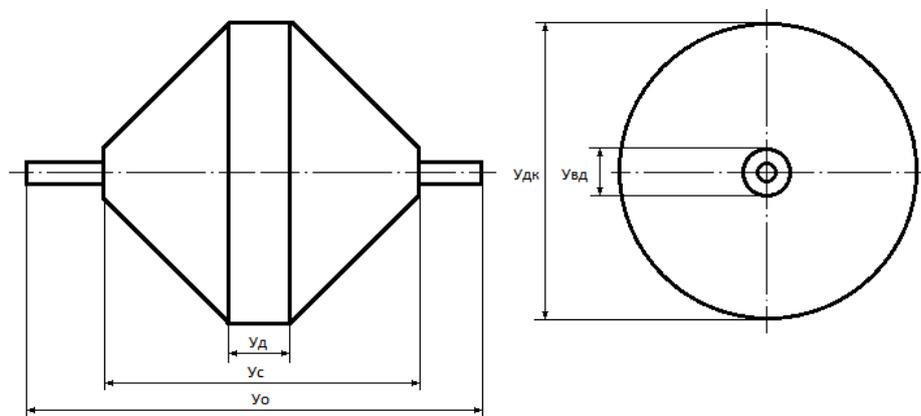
Основные конструктивные размеры уплотнителя стен и дна арыка.
